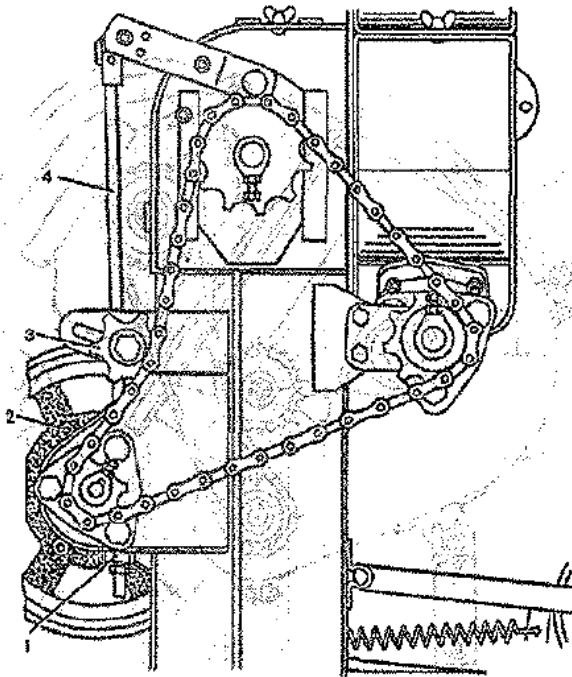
Регулировка привода элеватора: 1 - гайка; 2 - пружина предохранительной муфты; 3 - звездочка натяжная; 4 - тяга
